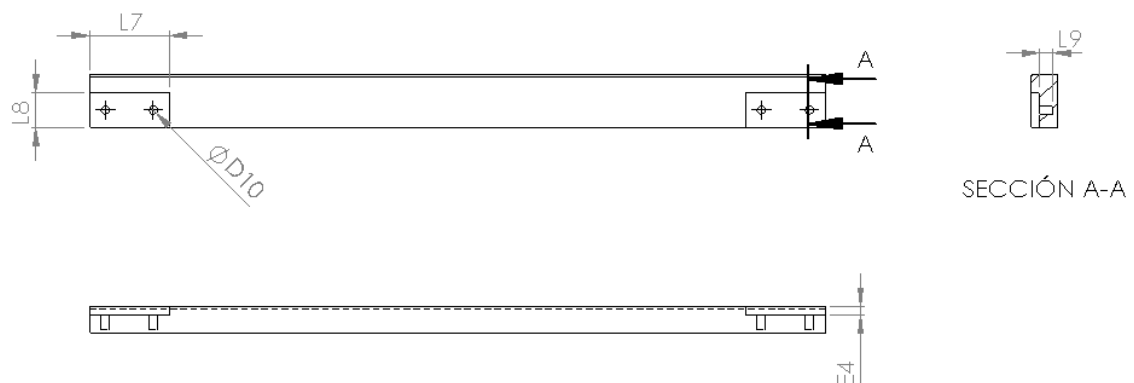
Croquis de dimensiones. Elemento 1.2.4.
